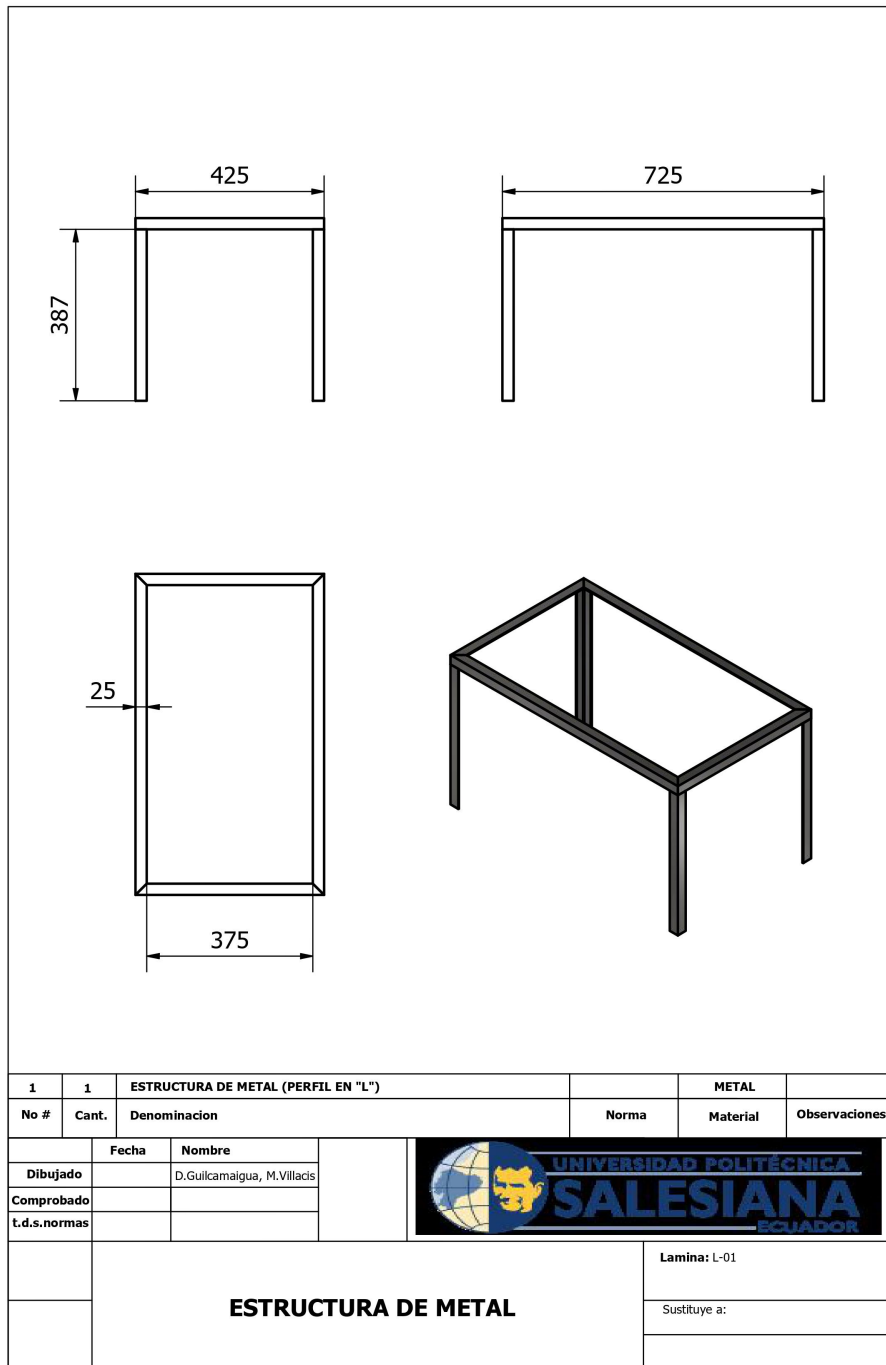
Plano de la estructura de perfil metálico. Fuente: Los autores
